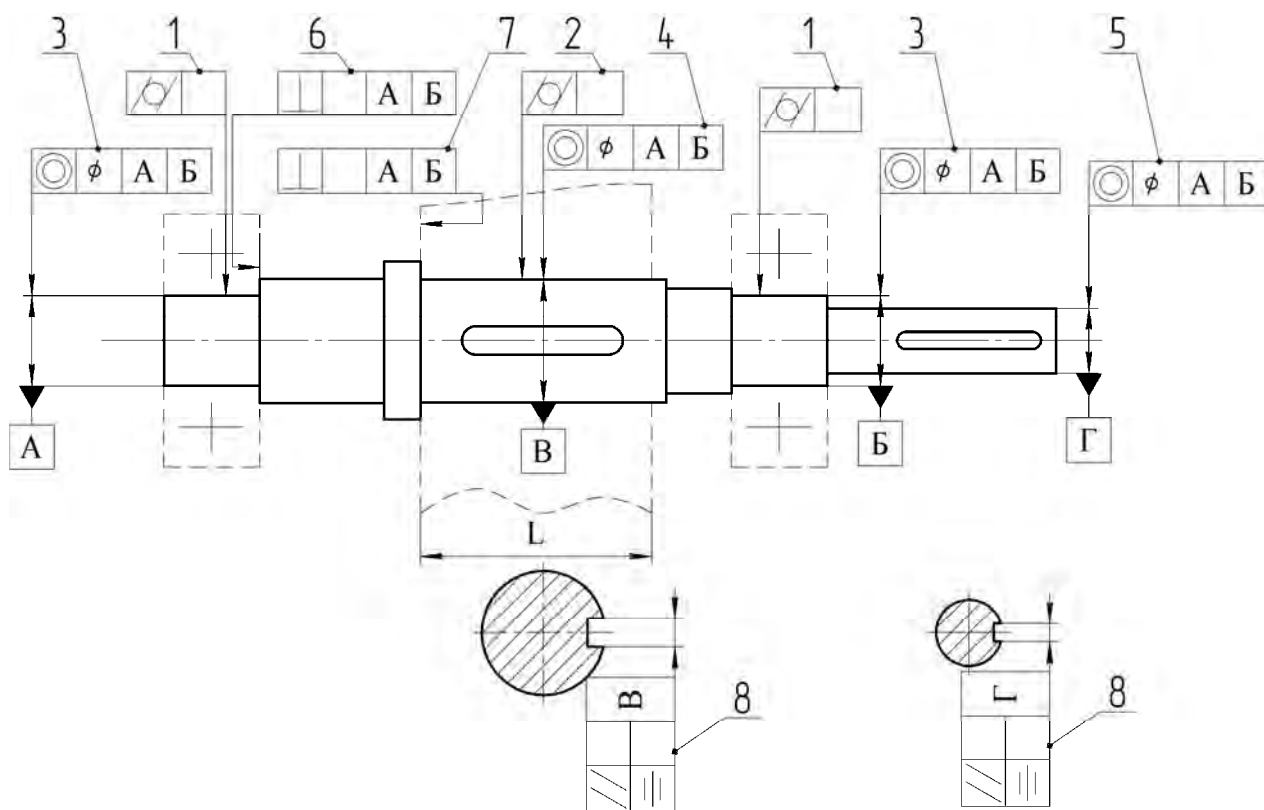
Допуски формы и расположения поверхностей вала
